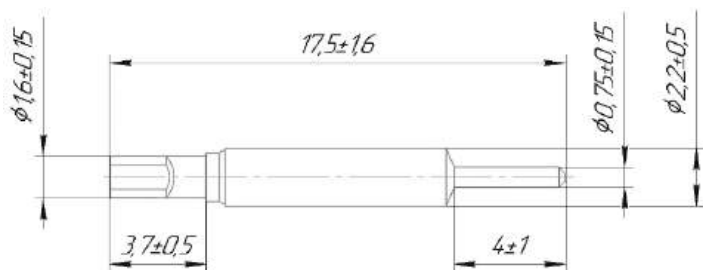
Габаритные размеры фильтров Ф26, типоразмер 1
